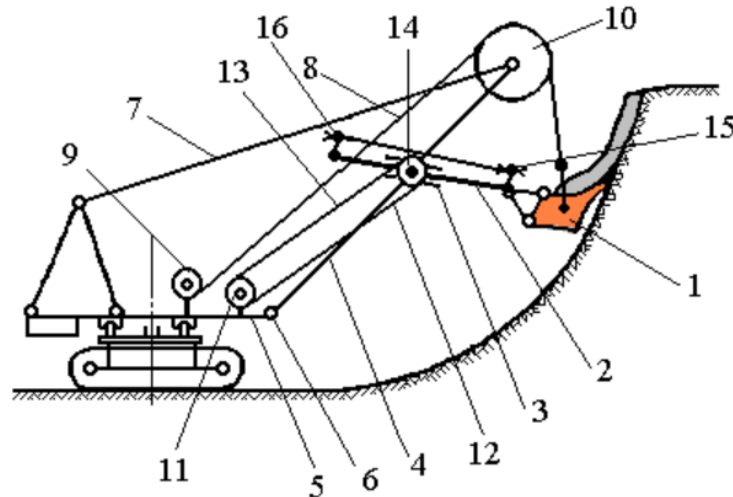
Конструктивна схема прямої напірної лопати з висувною рукояттю та канатним механізмом напору: 1 – ківш; 2 – рукояття; 3 – сідловий підшипник; 4 – стріла; 5 – поворотна платформа; 6 – шарнір; 7 – підвіска стріли; 8 – підйомний канат; 9 – лебідка підйому ковша; 10 – головний блок; 11 – напірна лебідка; 12, 13 – канати висунання рукояті; 14 – центральний блок; 15 – передній напівблок; 16 – задній напівблок.
